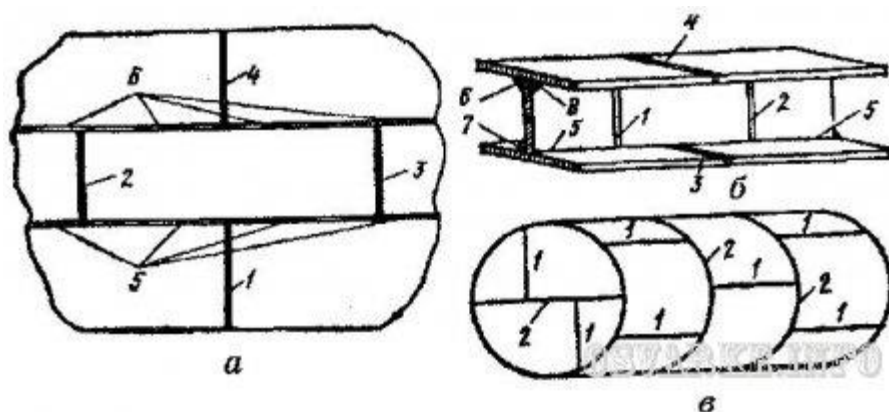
Последовательность наложения швов (1-8) при сварке: а - полотно из отдельных листов; б - двутавровой балки; в - цилиндрического сосуда
